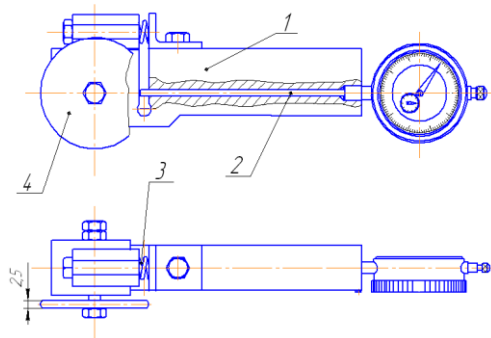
Однороліковий пристрій для обкатки з пружинною державкою: 1 – державка, 2 – щуп, 3 – пружина, 4 – ролік для обкатки
